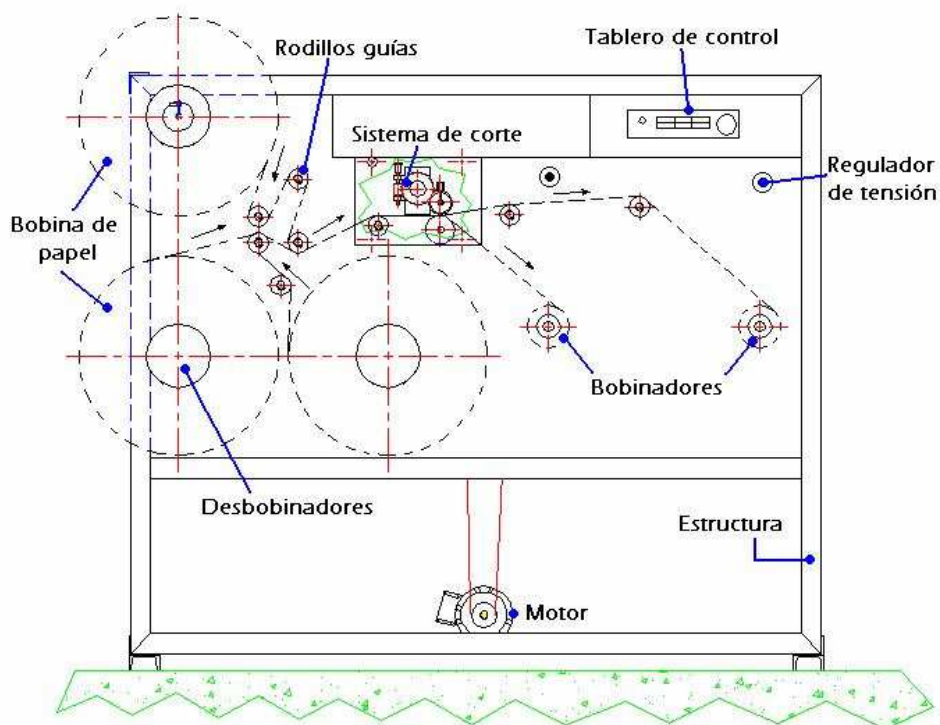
Vista frontal de la máquina cortadora rebobinadora de papel<sup>22</sup>.
